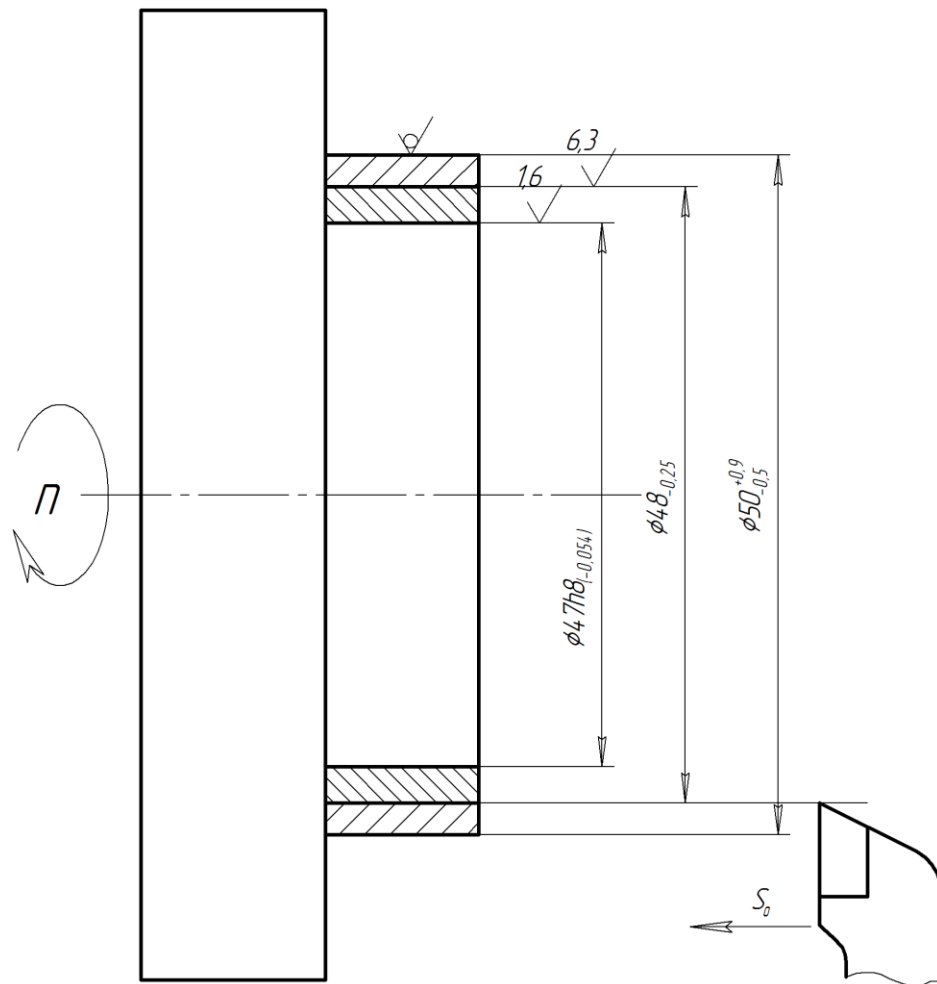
Схема обробки поверхні $\varnothing 47h11$
